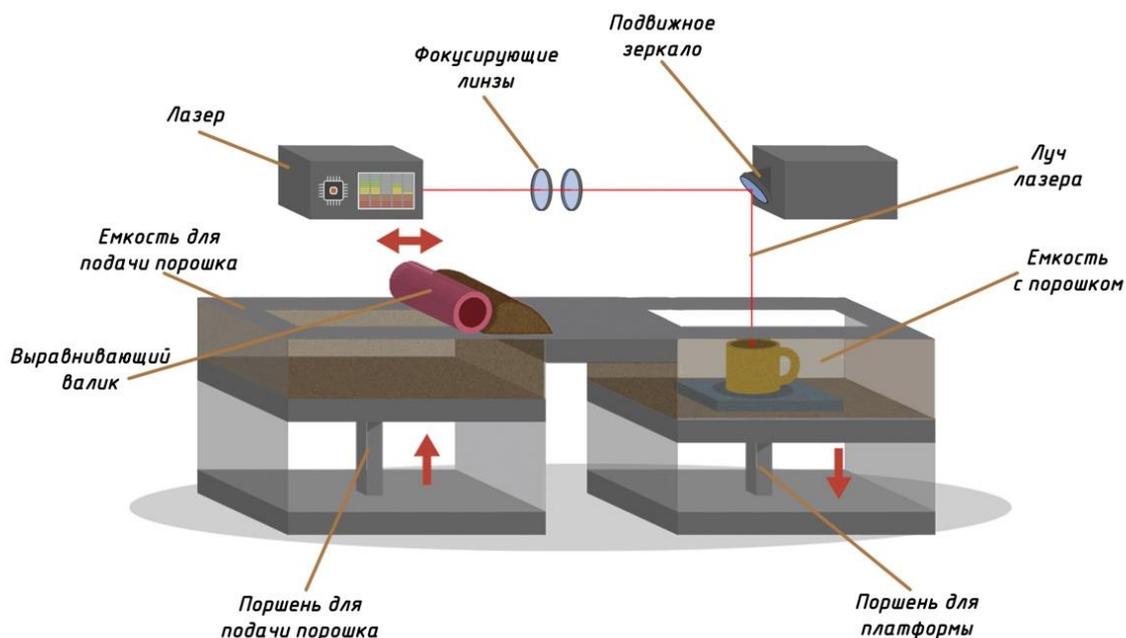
Принцип работы 3D-печати расплавлением порошкового материала
